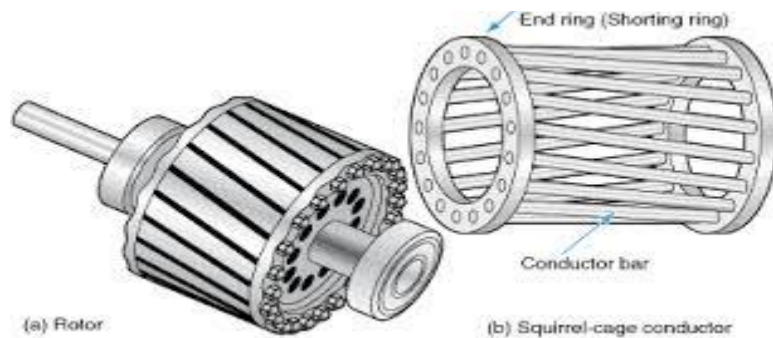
Schéma d'un rotor a cage d'écureuil
